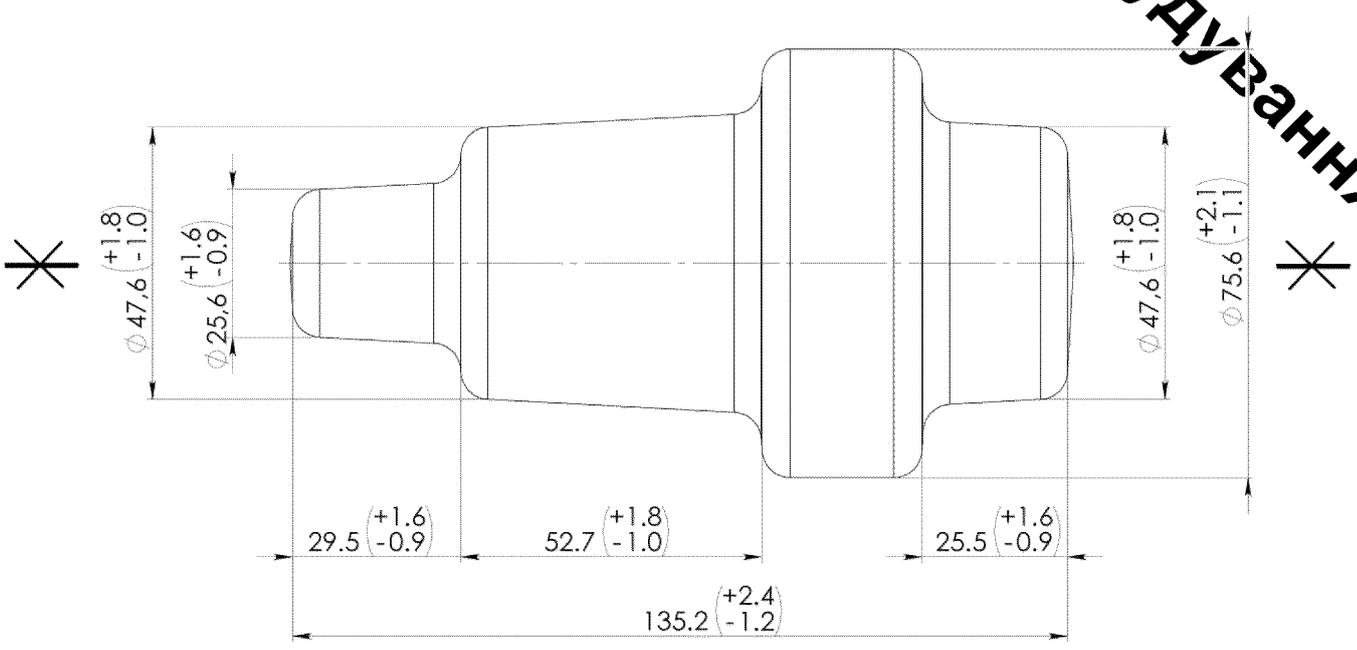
Ескіз заготовки деталі «Вал-шестерня Д02210.5»
